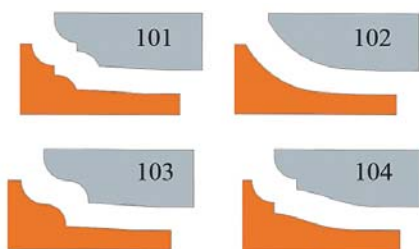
Комплект 011.03.00.00.000 — филинчатая фреза со сменными ножами
